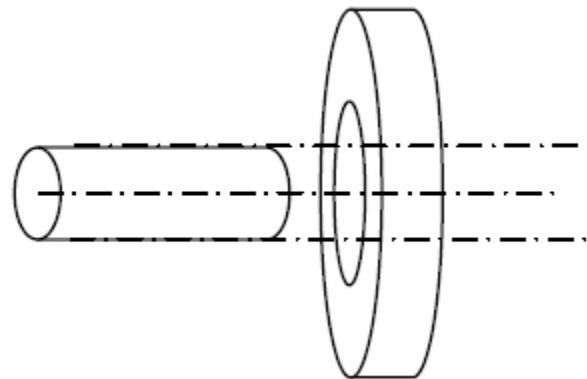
Materiales necesarios para el proyecto de construcción del parlante. Fuente: Guía para la construcción de un parlante de Tony Peñarredonda
